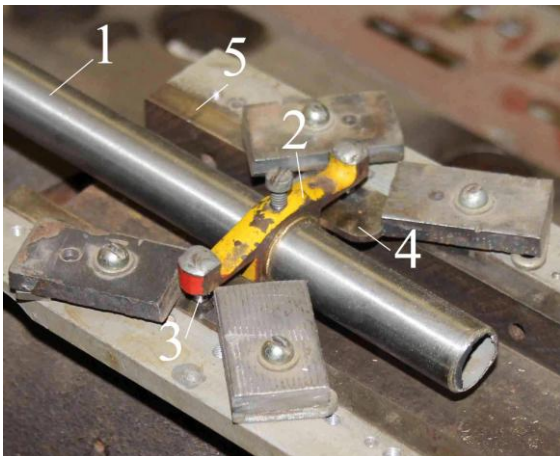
Конструкция шарнирной опоры типа «иголка»: 1 – исследуемая трубка; 2 – корпус опоры; 3 – «иголка»; 4 – пластина; 5 – плита
